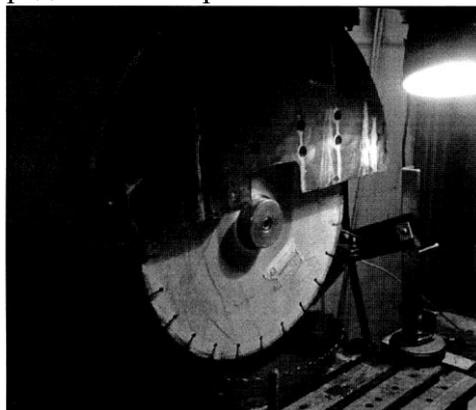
Общий вид установки для электрохимической правки алмазного круга
